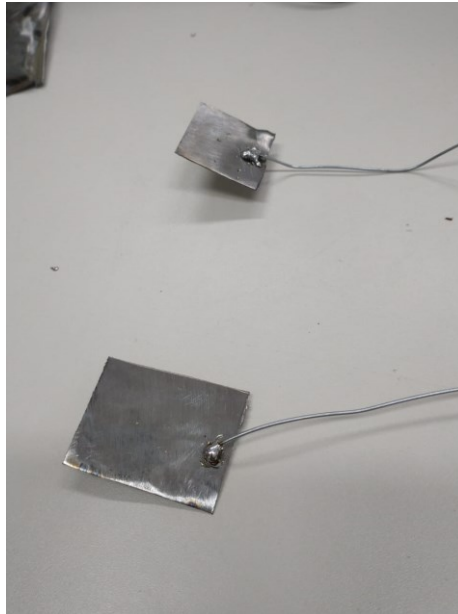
Chapas soldadas com o arame galvanizado.
